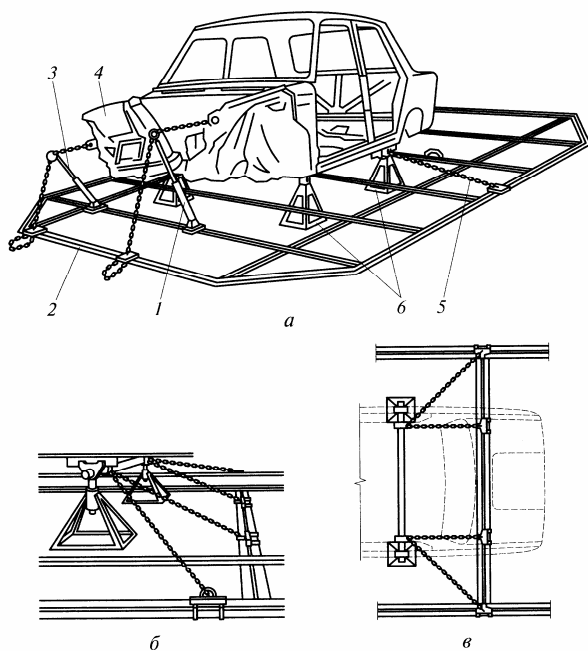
Напольная стапельная рама Р-620 для правки кузова легкового автомобиля: *а* — общий вид; *б* — схема закрепления за пороги кузова; *в* — схема запасовки цепей; 1, 3 — рабочие гидроцилиндры; 2 — основание; 4 — кузов; 5 — расчалочное приспособление; 6 — подставки
